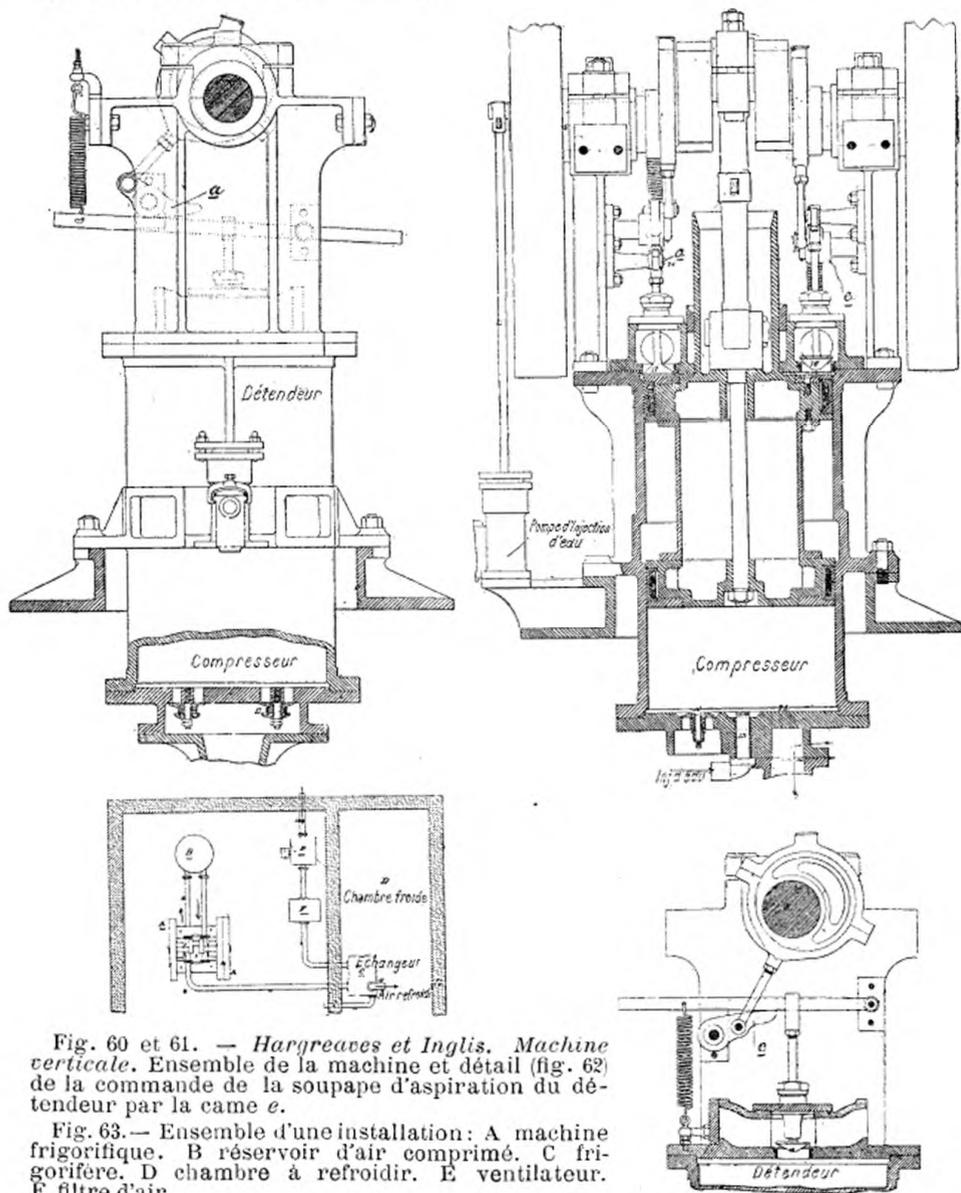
et 61. — Hargreaves et Inglis. Machine verticale. Ensemble de la machine et détail (fig. 62) de la commande de la soupape d'aspiration du détendeur par la came *e*.
